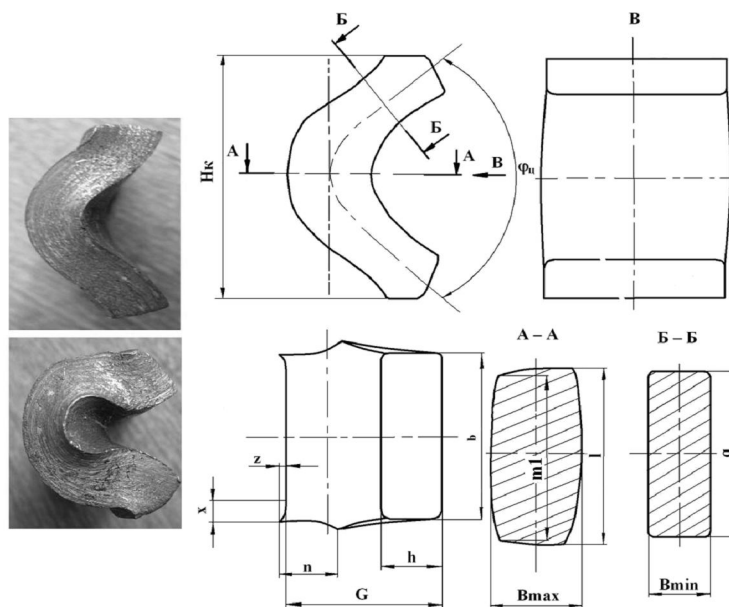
Схема продольного изгиба заготовок прямоугольного поперечного сечения:
